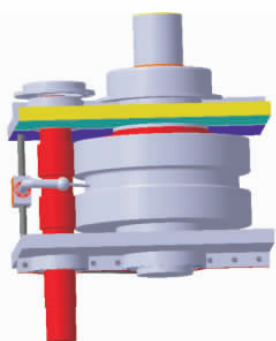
一级圆柱齿轮减速箱齿轮啮合部分三维示意图
